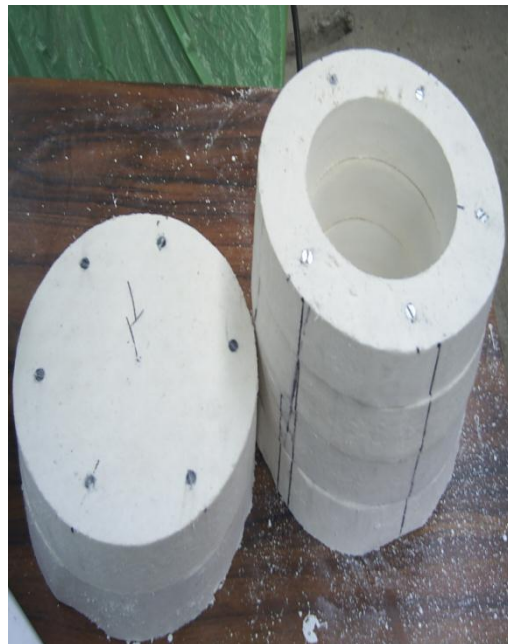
Aislante con tapadera para el crisol metálico.
